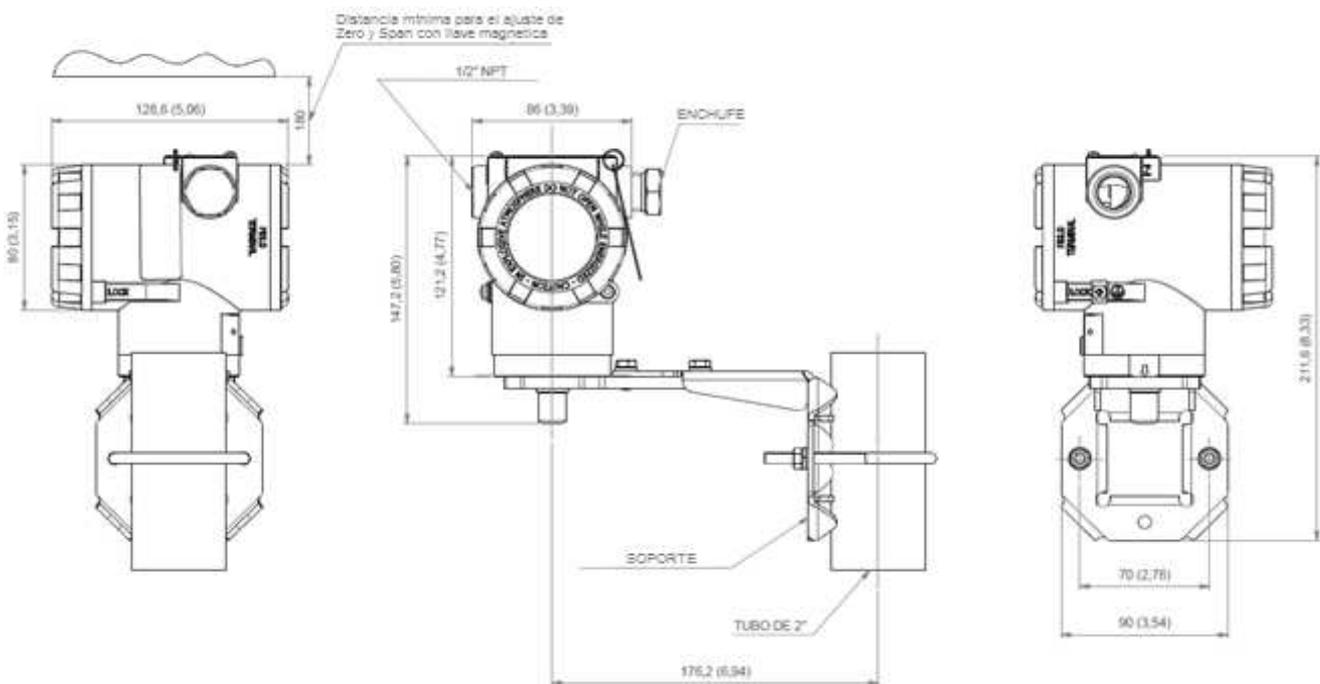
Esquema de dimensiones y montaje de VTP10-P.
